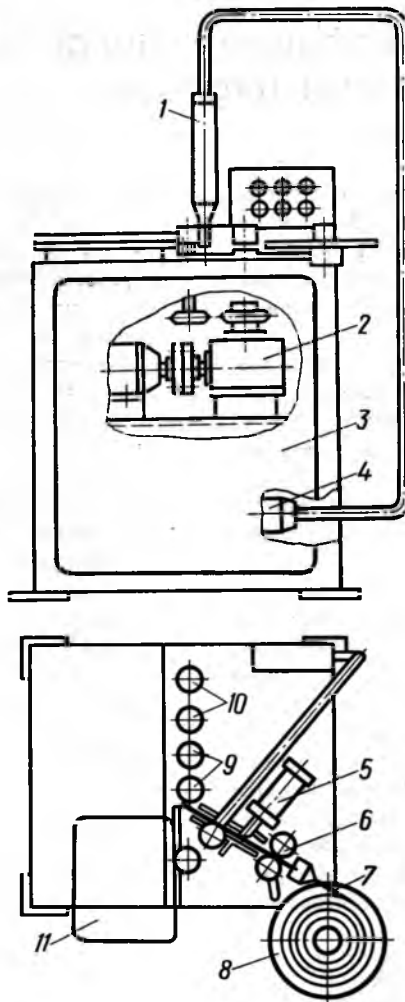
Станок для облицовывания кромок щитов небольших размеров:
